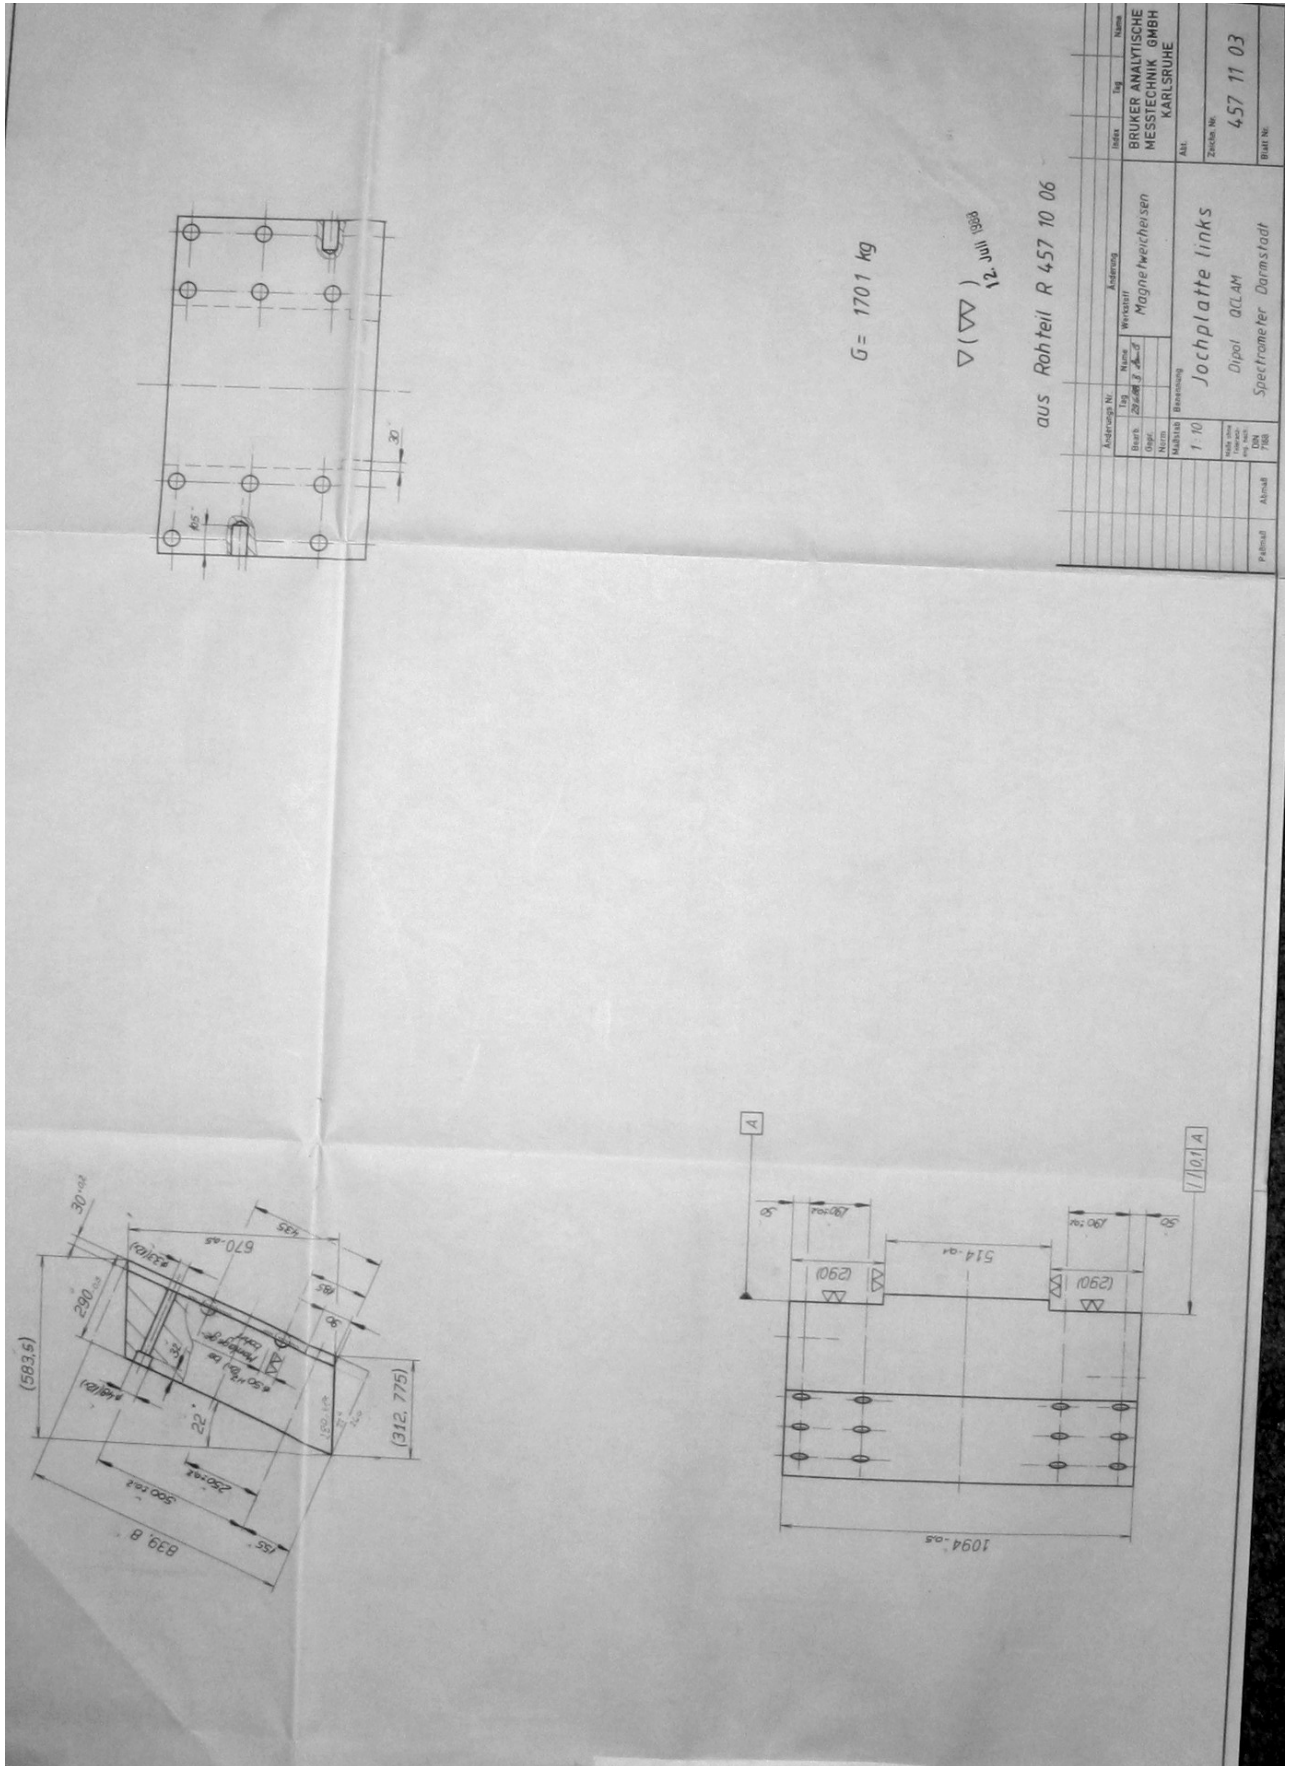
Technische Zeichnung der linken Jochplatte des QClams.
